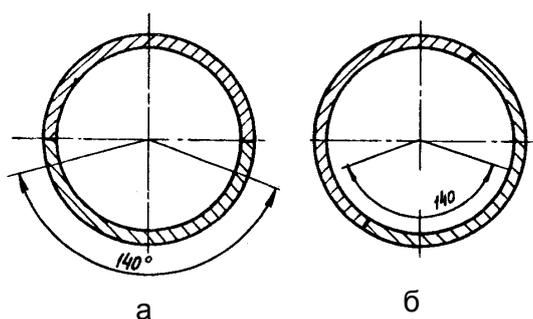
Расположение сварных соединений в нижней части оборудования и трубопроводов:
